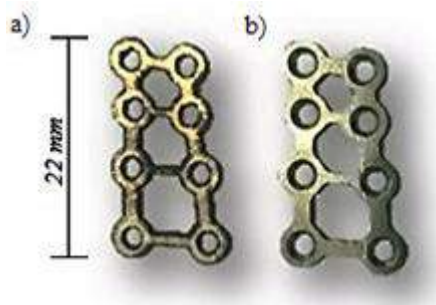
Produto usinado: a) Placa manufaturada usando uma máquina marcadora a *laser* de neodímio. b) Placa manufaturada pelo processo de usinagem CNC.
